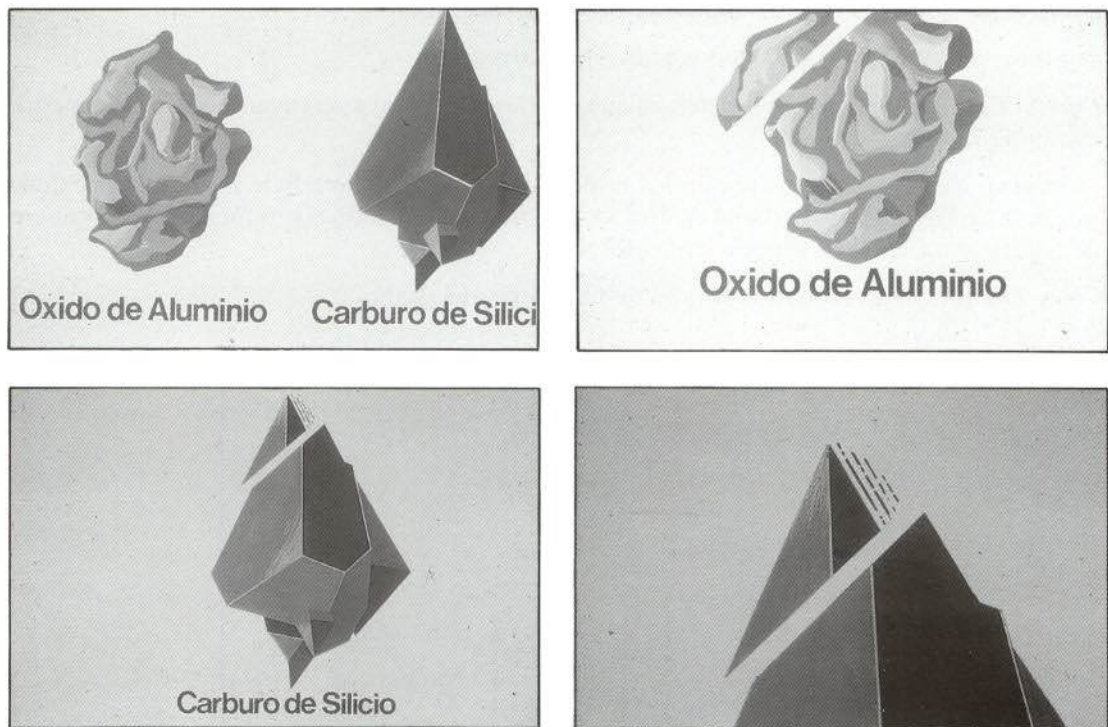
Oxido de aluminio y carburo de silicio: fracturas.
